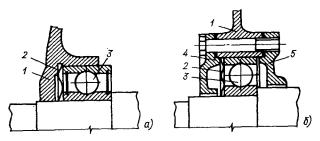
Подшипииковые узлы с иесквозным (а) и сквозным (б) отверстиями для посадки подшипников:
